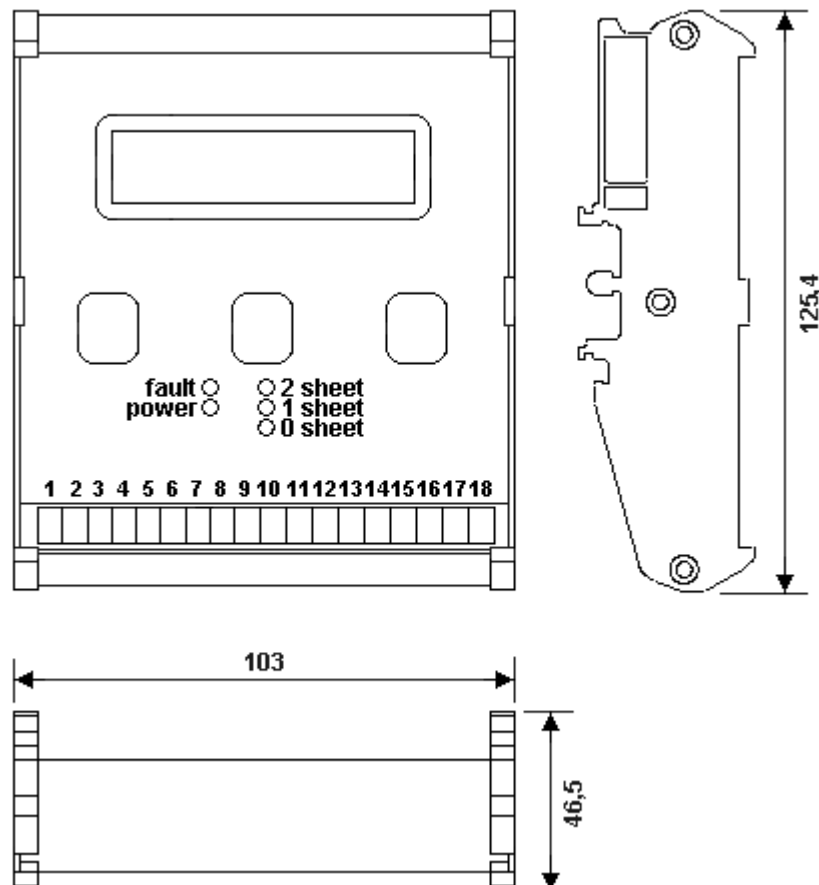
Dimensions de l'unité I100 (montage rail DIN)
